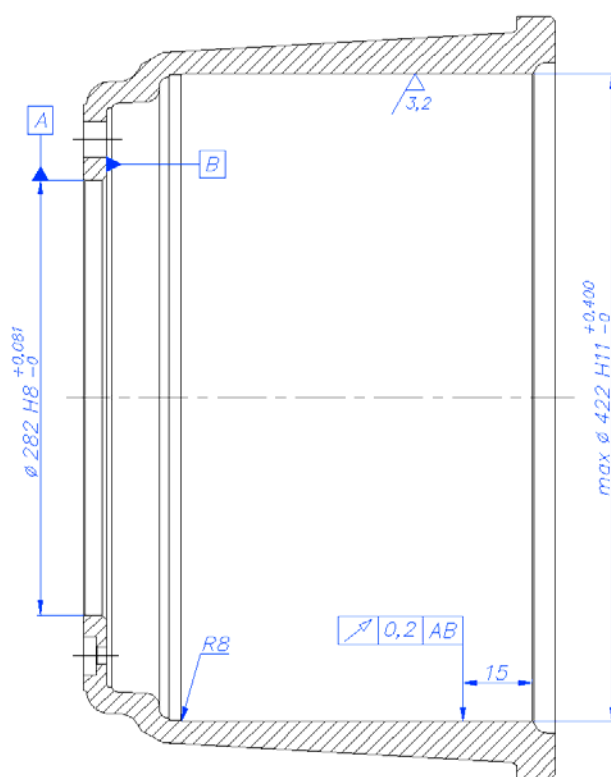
Размеры для обрабатывания барабана на токарном станке
